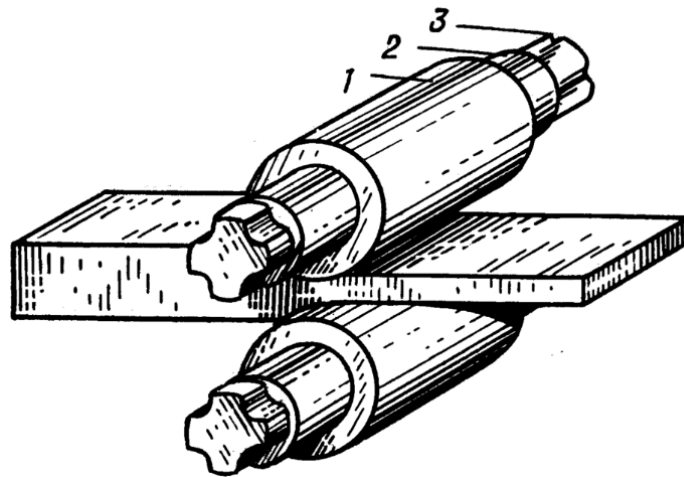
Елементи прокатного валка: 1 – бочка, 2- шийка, 3 – приводний кінець
